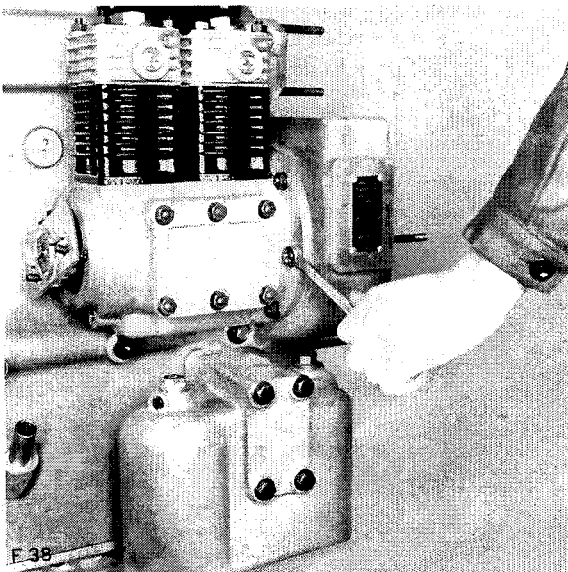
Lösen der Mutter auf dem Kettenrad für Luftkompressor- und Einspritzpumpenantrieb
